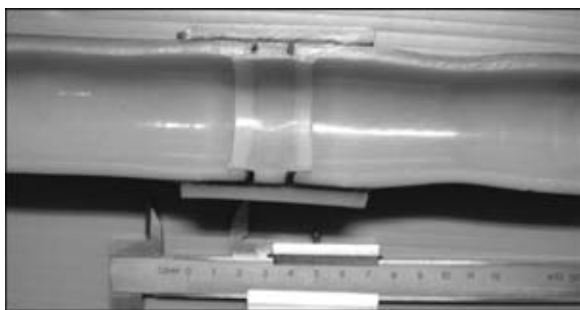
Продольное сечение соединения после проведения гидравлических испытаний
